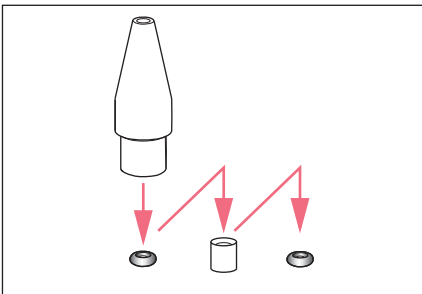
Desenho de corte com os anéis O-ring e a bucha distanciadora posicionados corretamente
